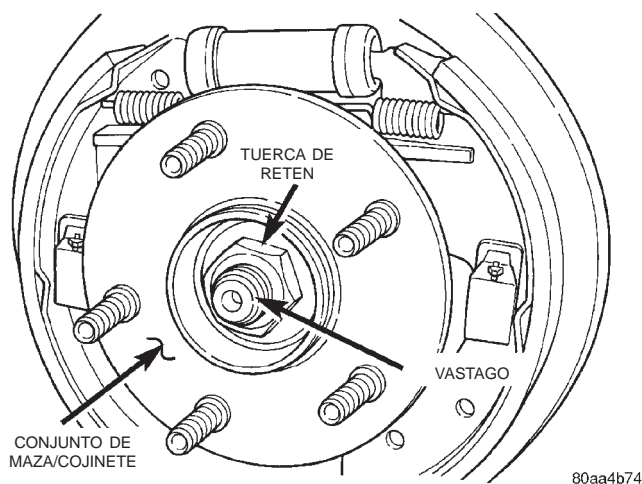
Tuerca de retén del conjunto de maza/cojinete
